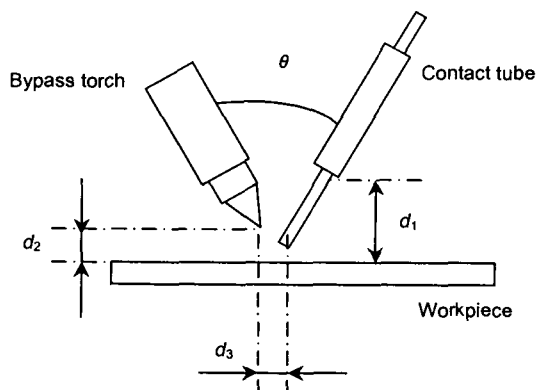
DE-GMAW 焊枪组合的几何参数
